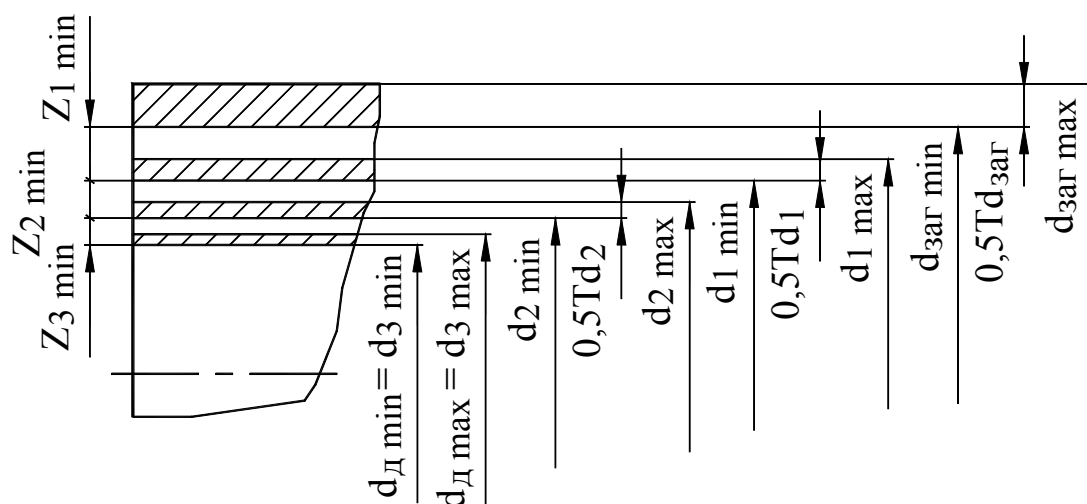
Схема расположения промежуточных припусков и допусков для цилиндрической детали
